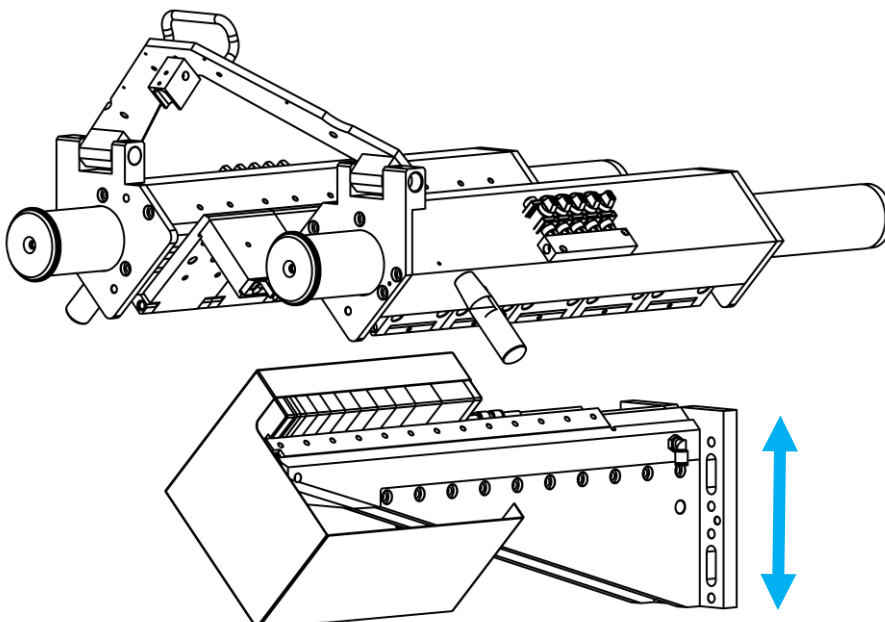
Holmhub pneumatisch mit 2-Handbedienung zum Einlegen abgekanteter Bauteile bis max. Schweißlänge (Standard Innenspannwerkzeugsatz).
